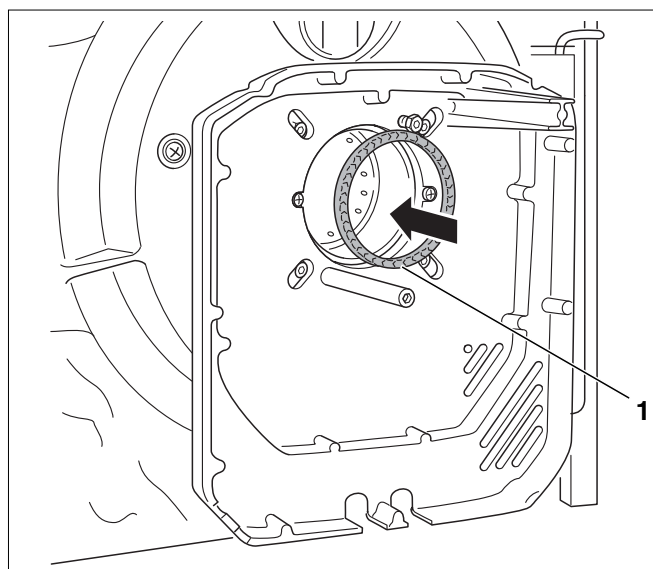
Colocación de la junta en los modelos de quemador 17 hasta 45
